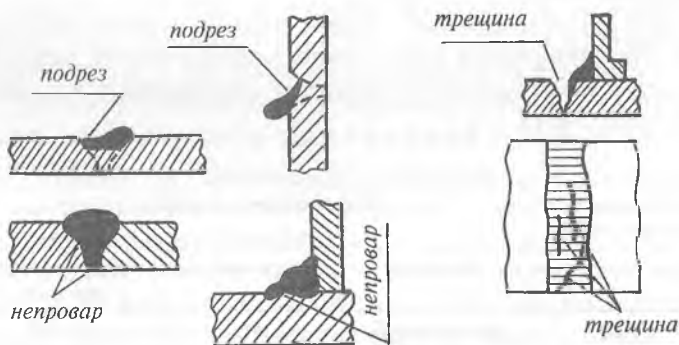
Дефекты сварки (затушеваны)
